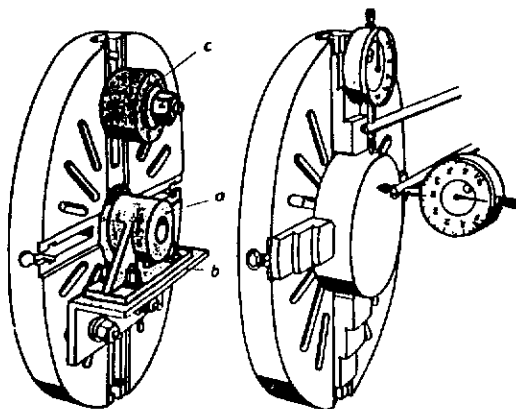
(izquierda). Sujeción por medio de soporte angular. a) Pieza; b) soporte angular para sujeción; c) contrapeso.
